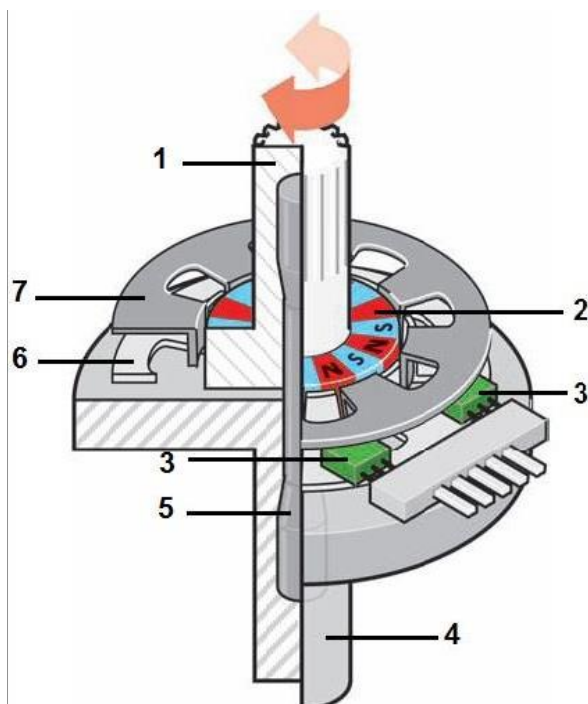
Сенсор кута повороту кермового колеса, заснований на ефекті Хола [4]: 1 - вхідний вал кермової колонки; 2 - кільцевий магніт; 3 - сенсор хола; 4 - вихідний вал-шестерня; 5 - торсійна вісь; 6 - перший статор; 7 – другий статор.
